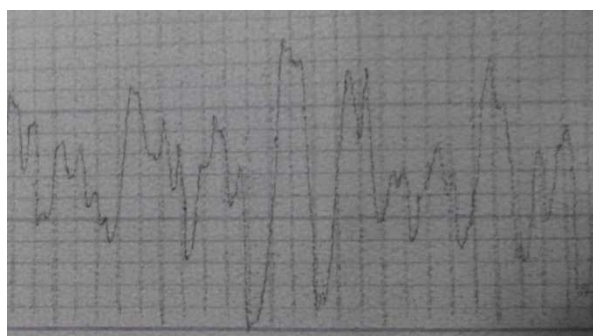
Профілограма обробленої поверхні циліндричного вала
